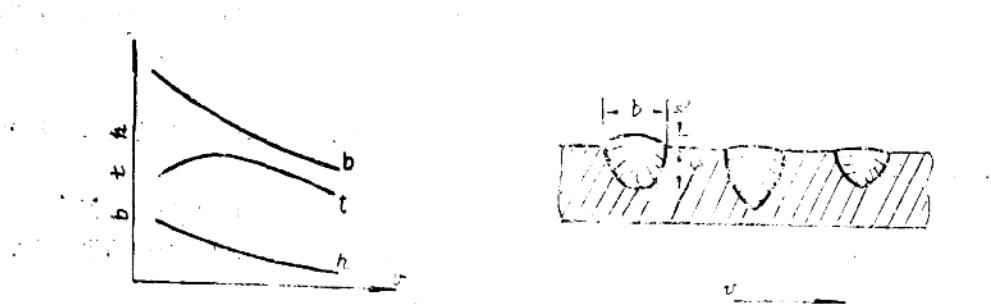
1—6 焊接速度V对焊缝形状的影响
